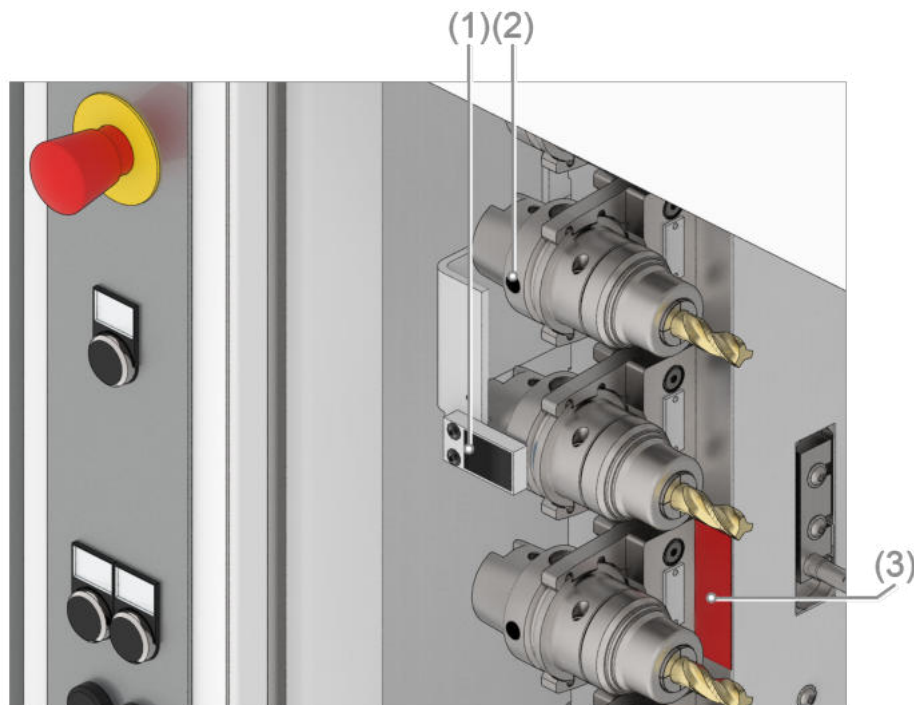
Hier am Beispiel einer Maschine mit Magazinbeladetür
